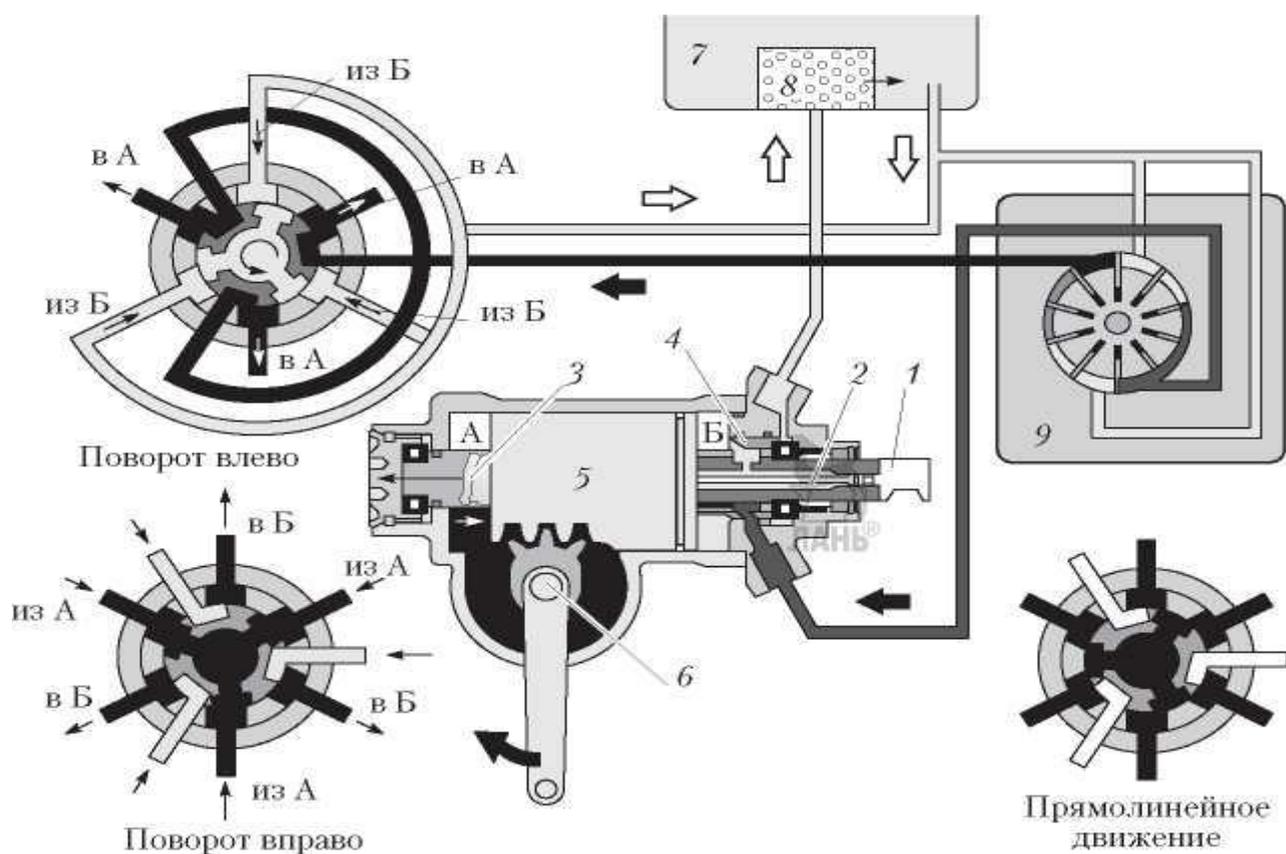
Схема гидроусилителя рулевого управления: 1 — вал-золотник; 2 — торсион; 3 — винт; 4 — гильза; 5 — поршень-рейка; 6 — вал сошки; 7 — масляный бачок; 8 — сетчатый фильтр; 9 — насос; А — полость силового цилиндра, находящаяся под давлением рабочей жидкости при повороте налево; Б — полость силового цилиндра, из которой рабочая жидкость уходит на слив при повороте налево.
